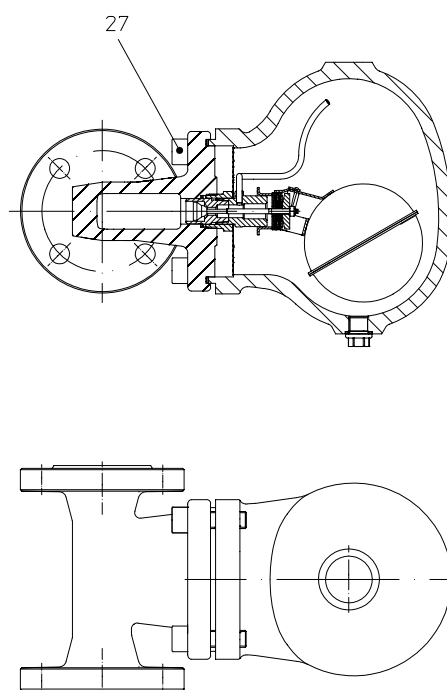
1 mit Flanschen - horizontale Einbaulage
